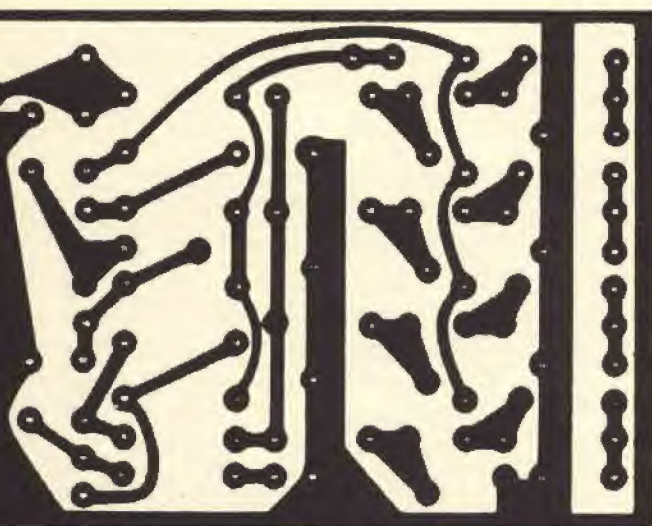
Il circuito stampato visto dalla parte del rame.
